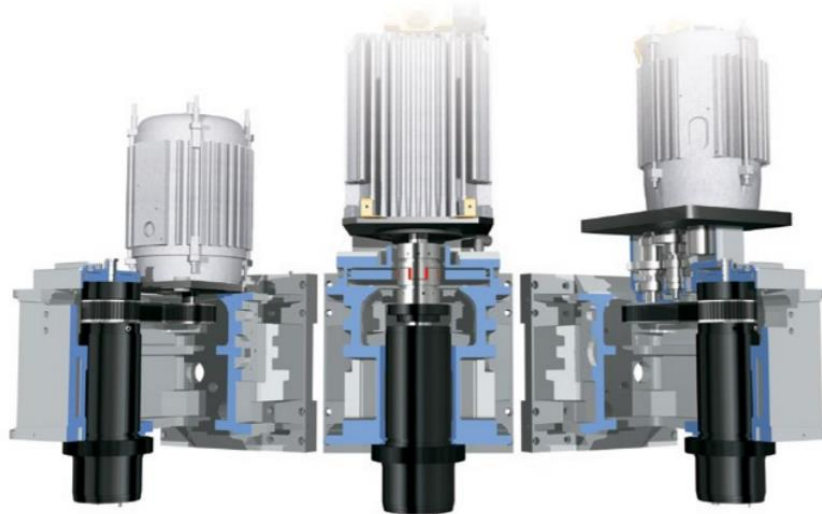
Шпинделі вертикально-фрезерних верстатів
